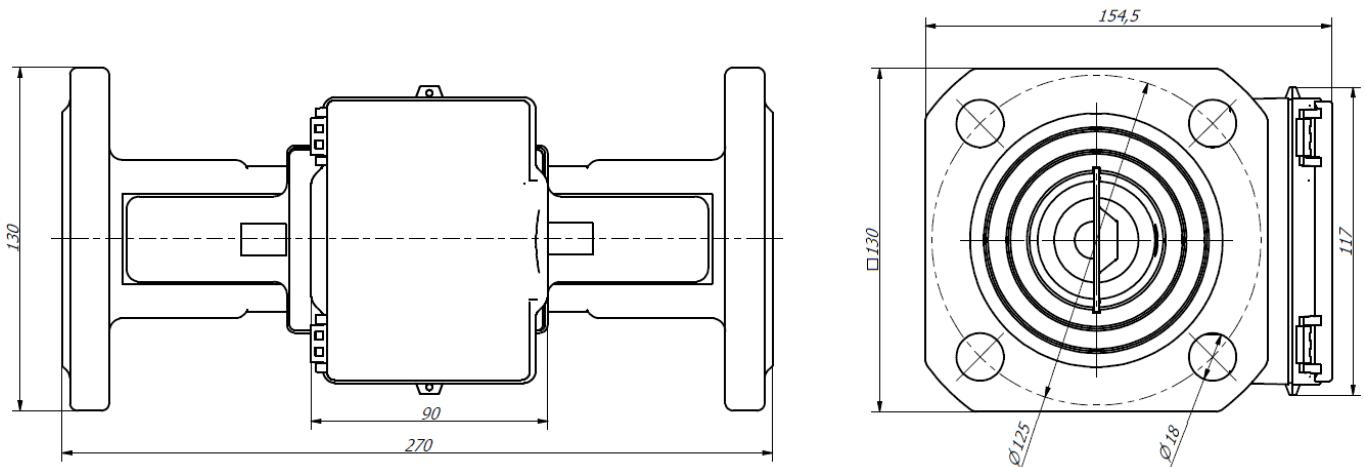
Flanschanschlüsse DN50, Baulänge L=270 mm
